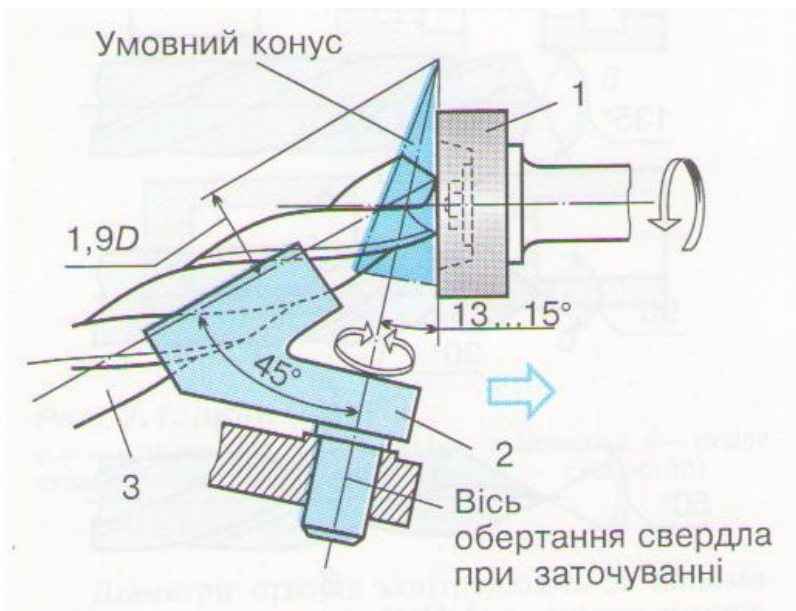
Схема заточування свердла на свердлозаточувальній верстаті:
